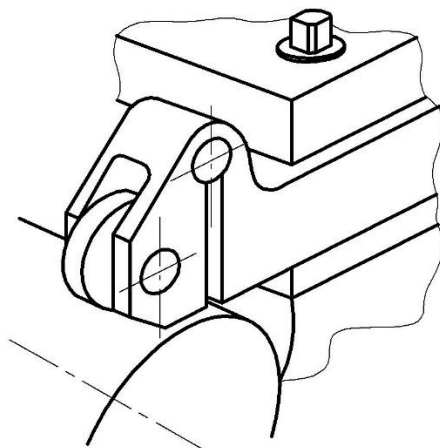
Схема обкатування вала пристосуванням з пружним корпусом
